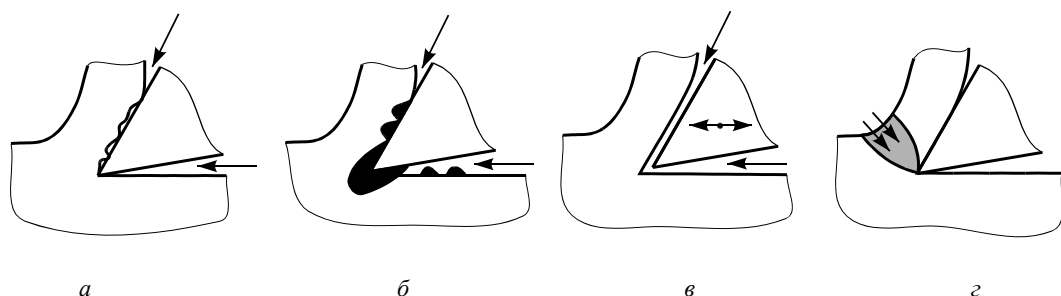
Схемы поступления смазочного материала в контактную зону при резании металлов [3]
